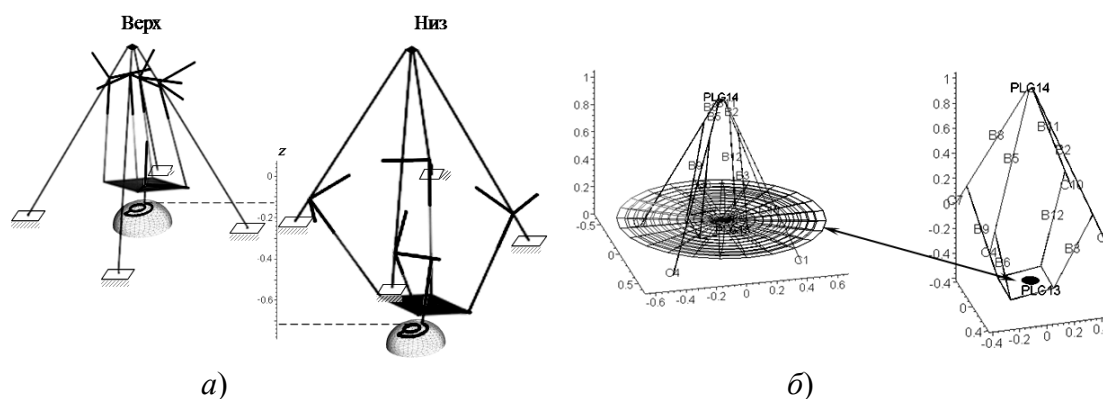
Можливі розташування заготовки по координаті z в робочому просторі верстату (а) і еліпсоїди податливостей при переході від верхнього розташування заготовки до нижнього (б)
